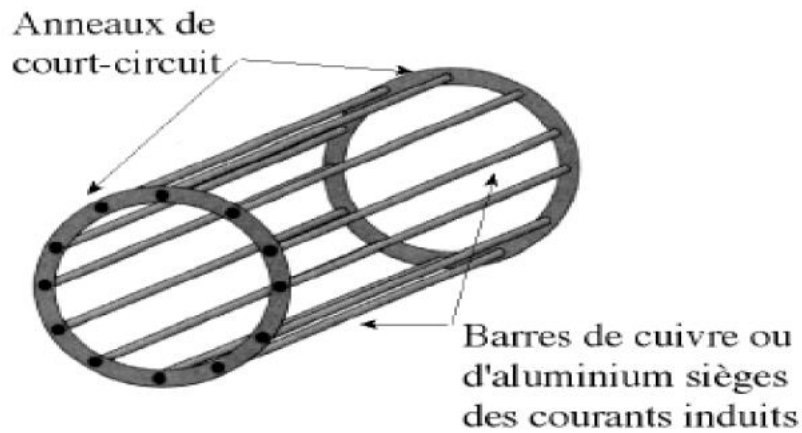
Vue schématique du rotor à cage d'écureuil
